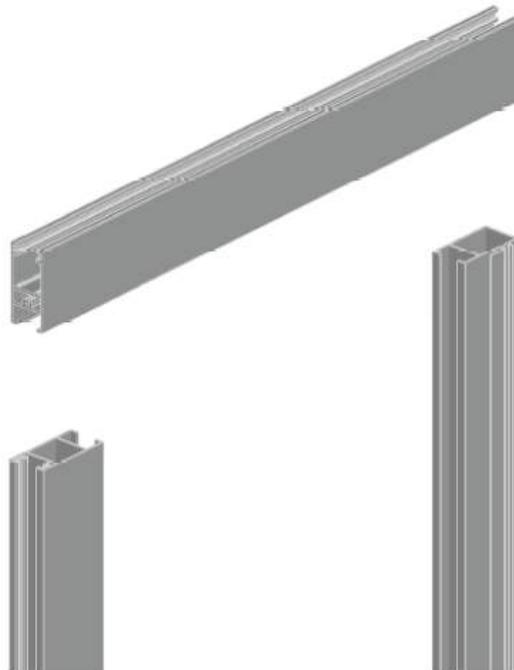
Perfiles de hoja con corte recto (lateral, horizontal y central).
